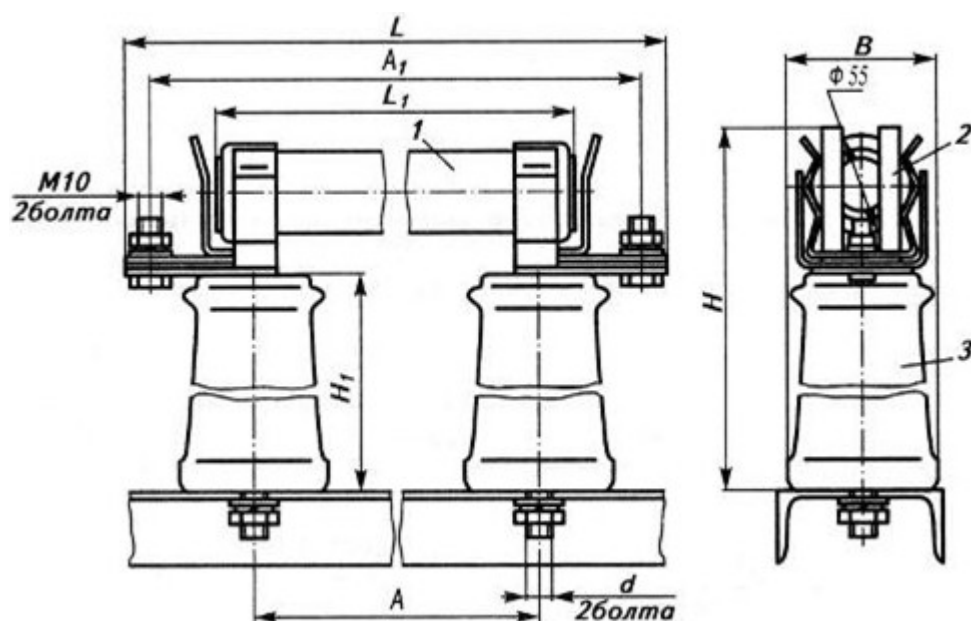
Габаритные, установочные и присоединительные размеры предохранителей серии ПКН001 (исполнение У3)1-патрон; 2-контакт; 3-изолятор
